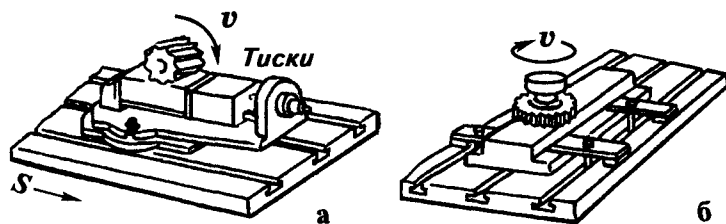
Фрезерование плоскостей: а – цилиндрической фрезой в тисках; б – торцевой фрезой на столе станка
